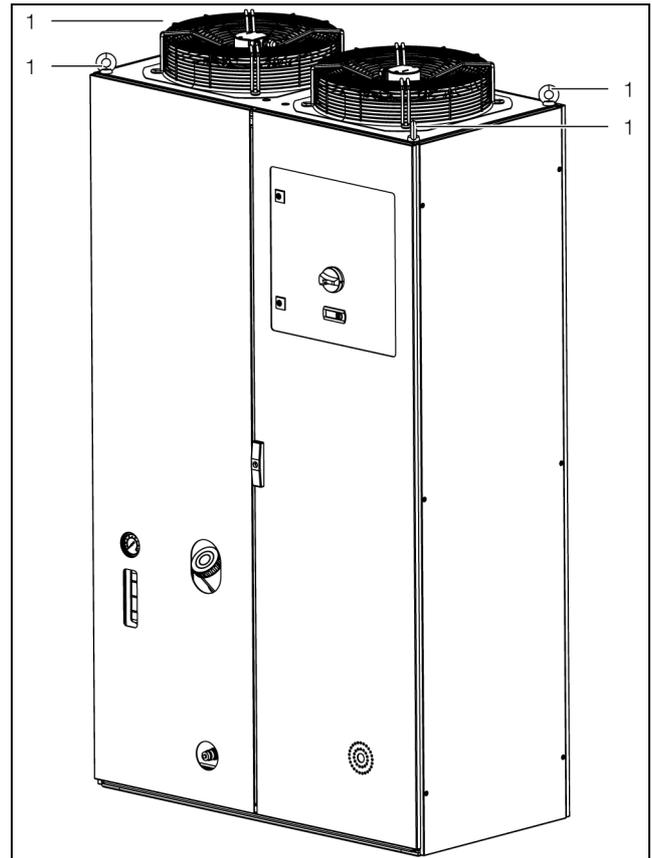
Augenschraube für Transport (3335.870, 3335.860)
